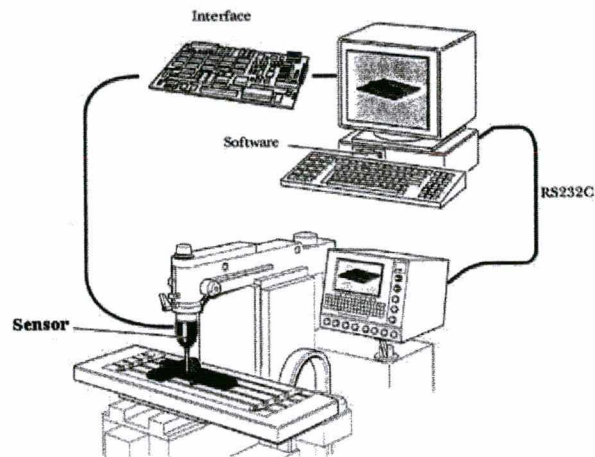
Sistema Retroskan (RENISHAW) em fresadora CNC
